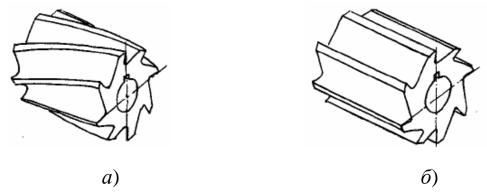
Разновидности наклона зубьев цилиндрической фрезы: с винтовым зубом (a) и с прямым зубом (δ)
